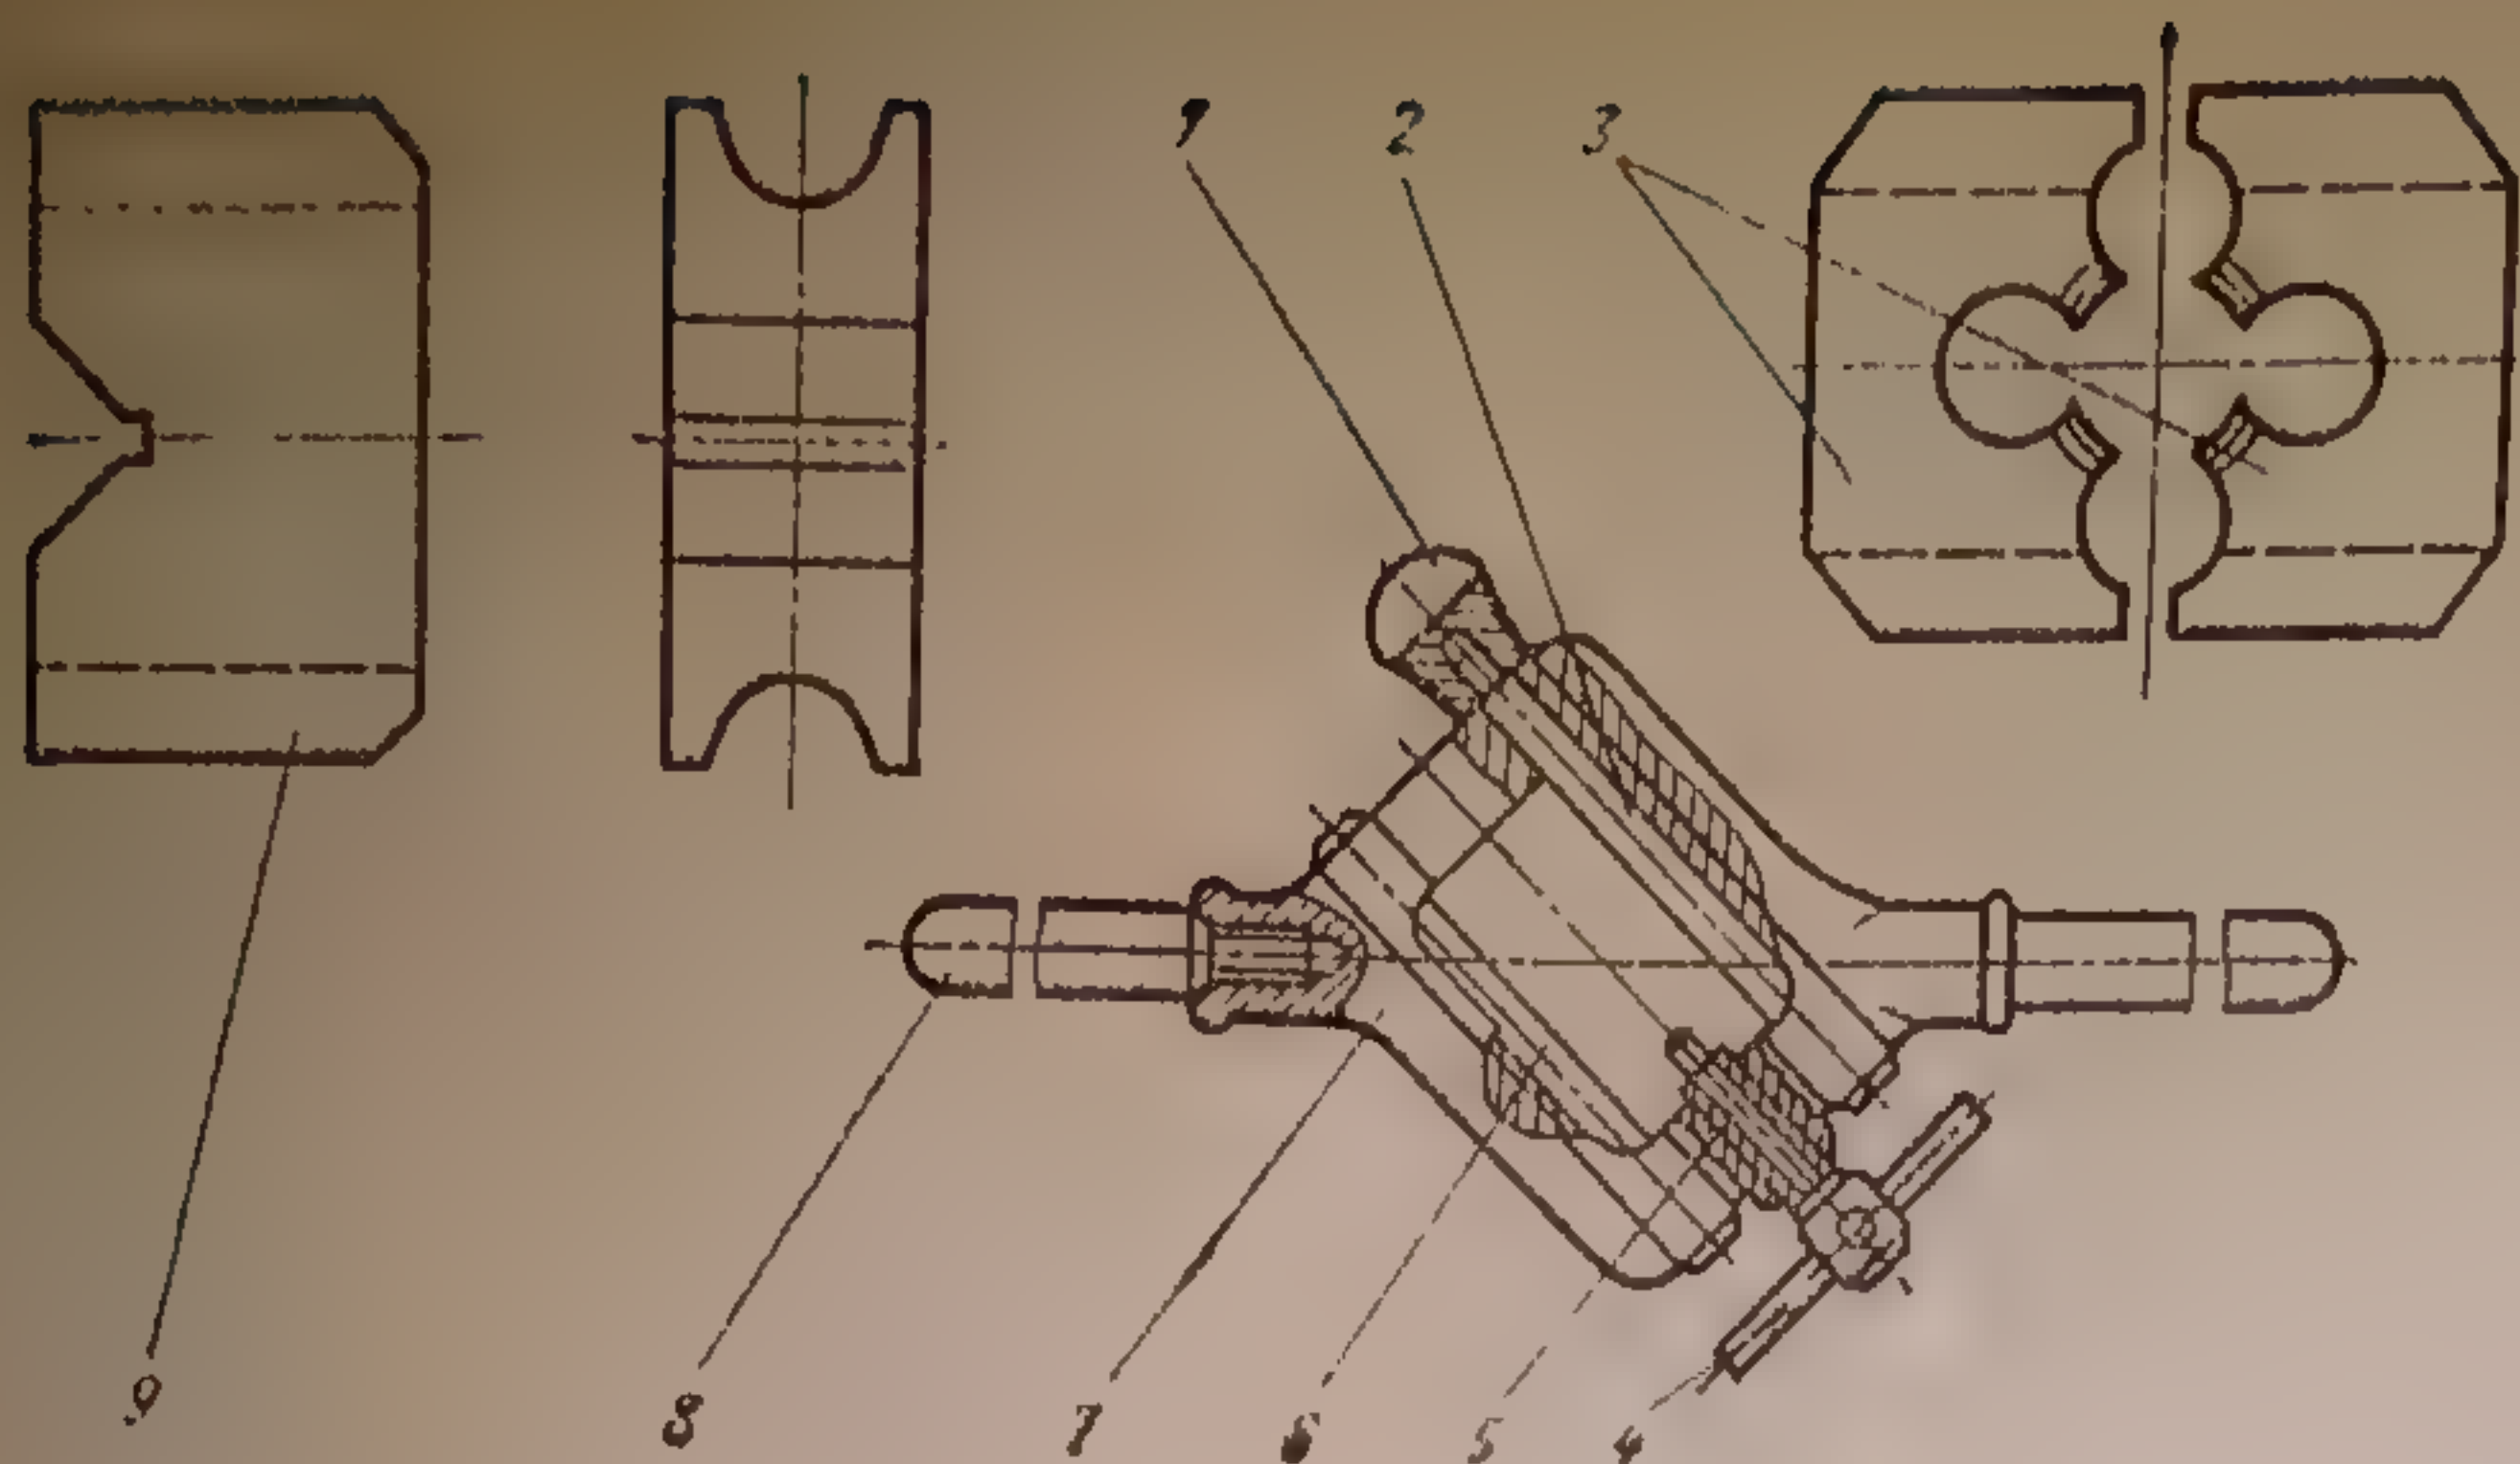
Косой клупп: 1 — головка штыря; 2 — штырь; 3 — плашка раздвижная; 4 — рукоятка винта; 5 — винт; 6 — штифт; 7 — корпус; 8 — рукоятка; 9 — сухарь
